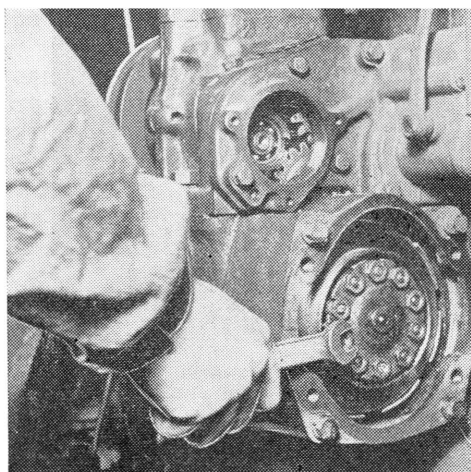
Регулировка муфты сцепления механизма передачи пускового двигателя при помощи регулировочных гаек
